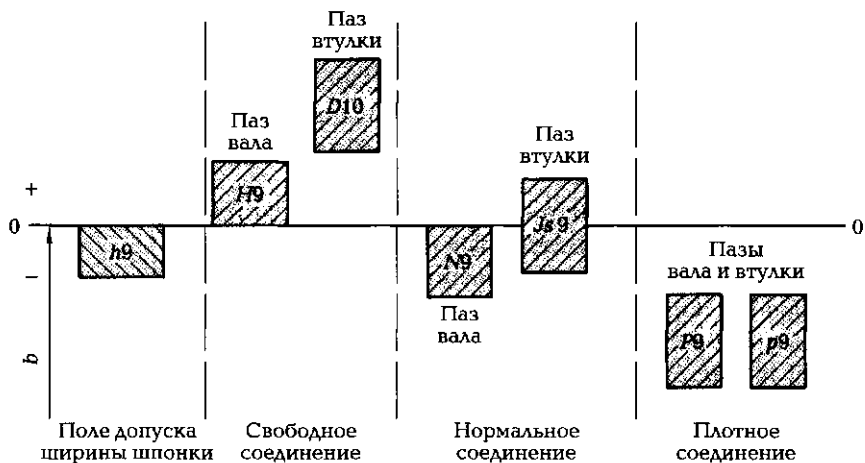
Схема расположения полей допусков по ширине шпонки
